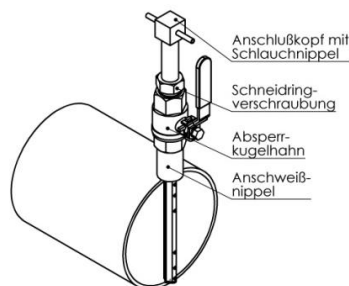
Aufbau einer FASTLOK-L-Sonde
